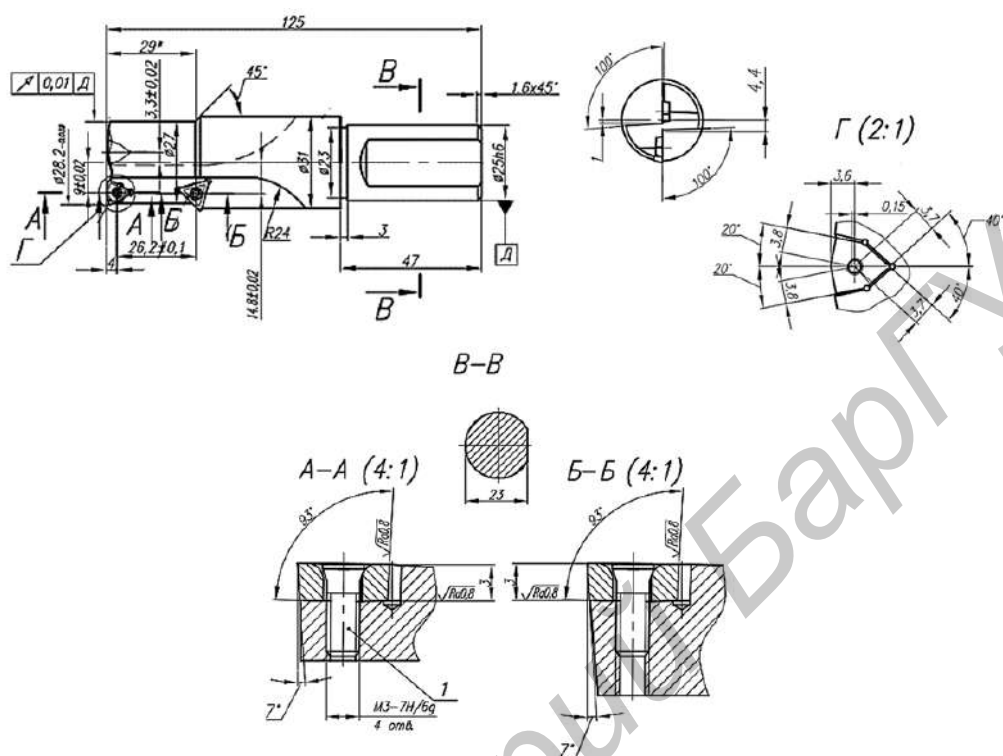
Конструкция ступенчатого комбинированного сверла с СНП
